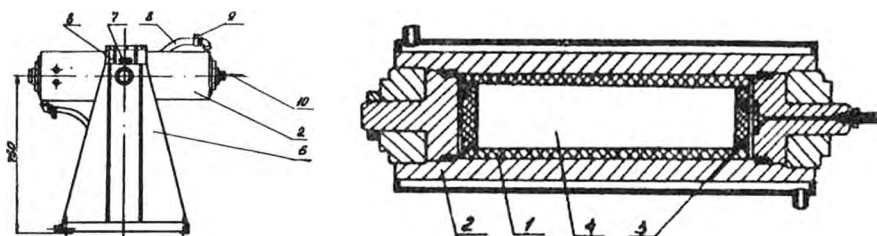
Универсальный реактор SVC-20. 1 — графитовая футеровка; 2 — корпус с двумя резьбовыми затворами (3); 4 — рабочий объем; 5 — станина; 6 — шарнирный узел; 7 — фиксирующий узел; 8, 9 — система водоохлаждения; 10 — система ввода и вывода газа
